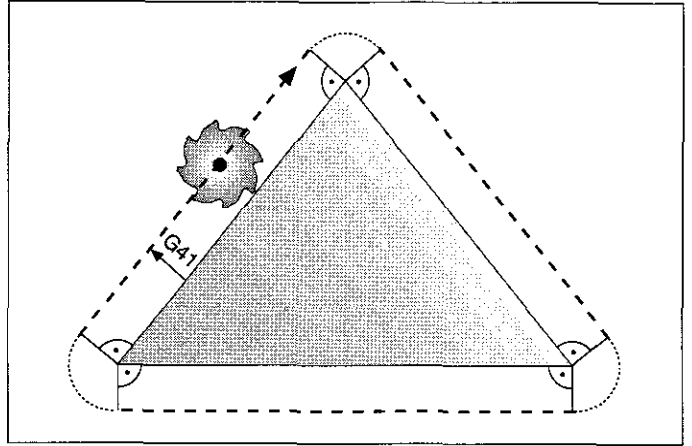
Werkzeug wälzt sich an Außenecken ab
